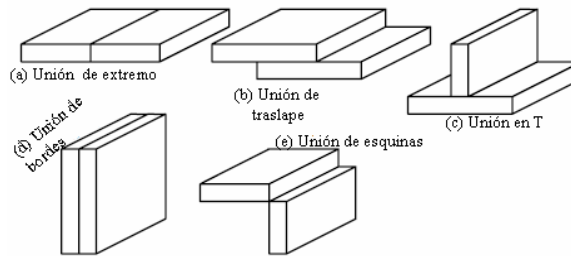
Tipos básicos de diseño de uniones soldadas: a) por extremos, b) por traslape, c) en T, d) por bordes, d) por esquinas [11].
